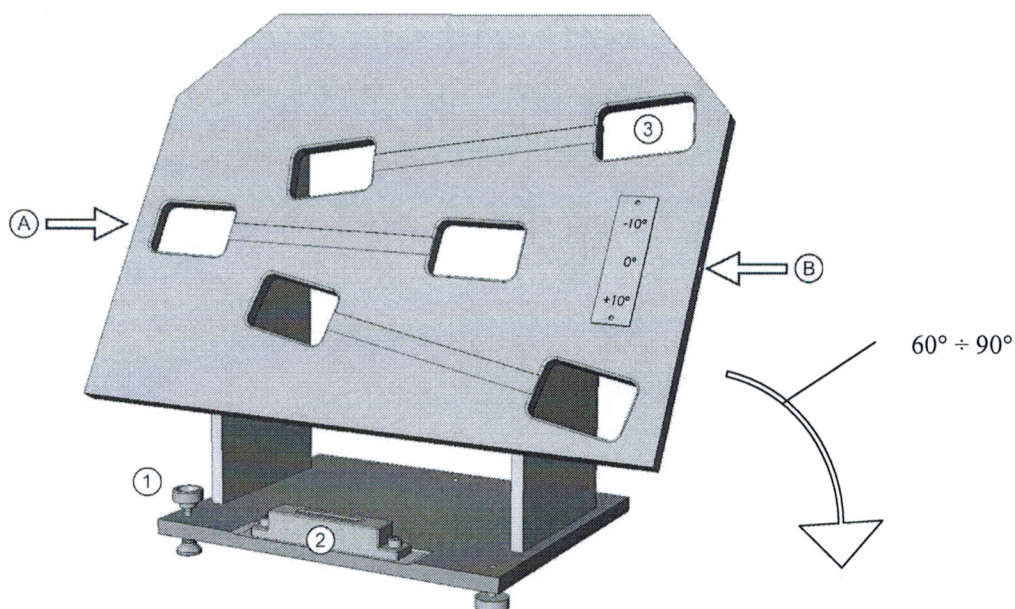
Калибровочное приспособление для имитации углов поворота рулевого колеса (1 - установочные винты; 2 – уровень; 3 - отверстия для зажимных рычагов; А / В - вспомогательные отверстия)
